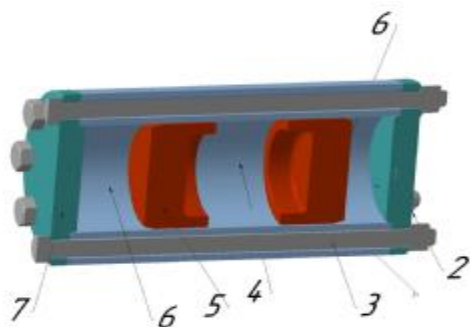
Модель трехкамерный контейнер для многостадийного совместимого взрывоударного дробления кусковых твердосплавных отходов: 1 – цилиндр; 2 – гайка; 3 – болт стяжной; 4 – камера взрывная; 5 – поршень-ударник; 6 – камера ударная; 7 – крышка
